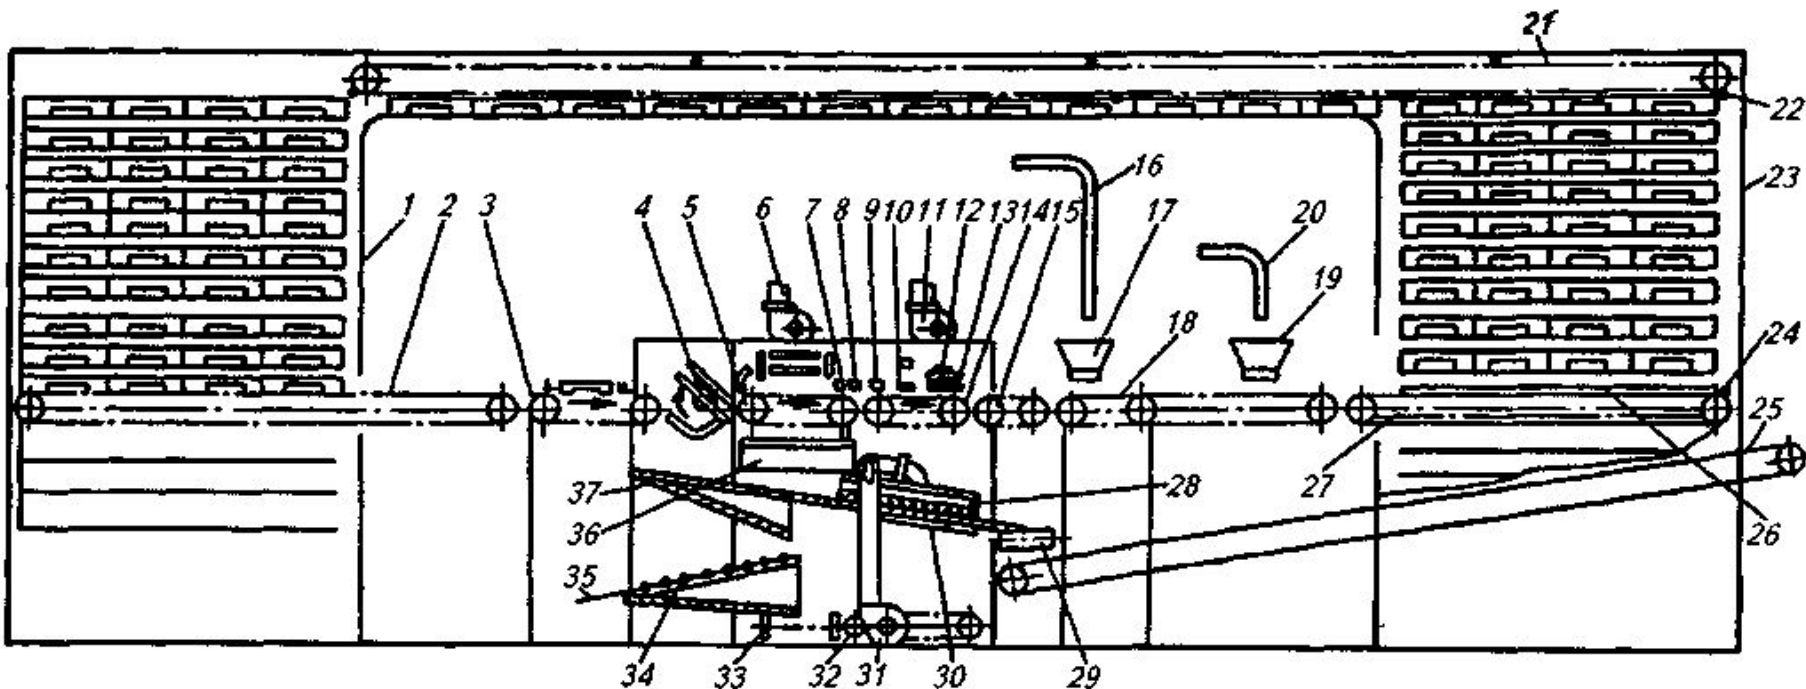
Установка фирмы «Сави-Жан-Жан» для отливки конфетных корпусов в крахмальные формы с ускоренной выстойкой корпусов.
